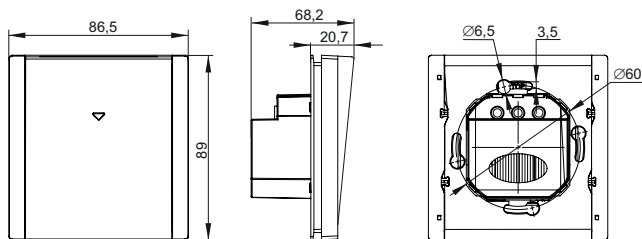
Габаритные и установочные размеры выключателя / Figure 1 – Overall and installation dimensions of the switch / 1-сурет – Ажыратқыштың габариттік және орнату өлшемдері / Figura 1 - Dimensiunile generale și de instalare ale întrerupătorului / Зурар 1 - Унтраалгын овор ба суурилуулах хэмжээ / 1-rasm - Viklyuchatelning gabaritlari bo'yicha va o'rnatilish natijasidagi o'lchamlari
